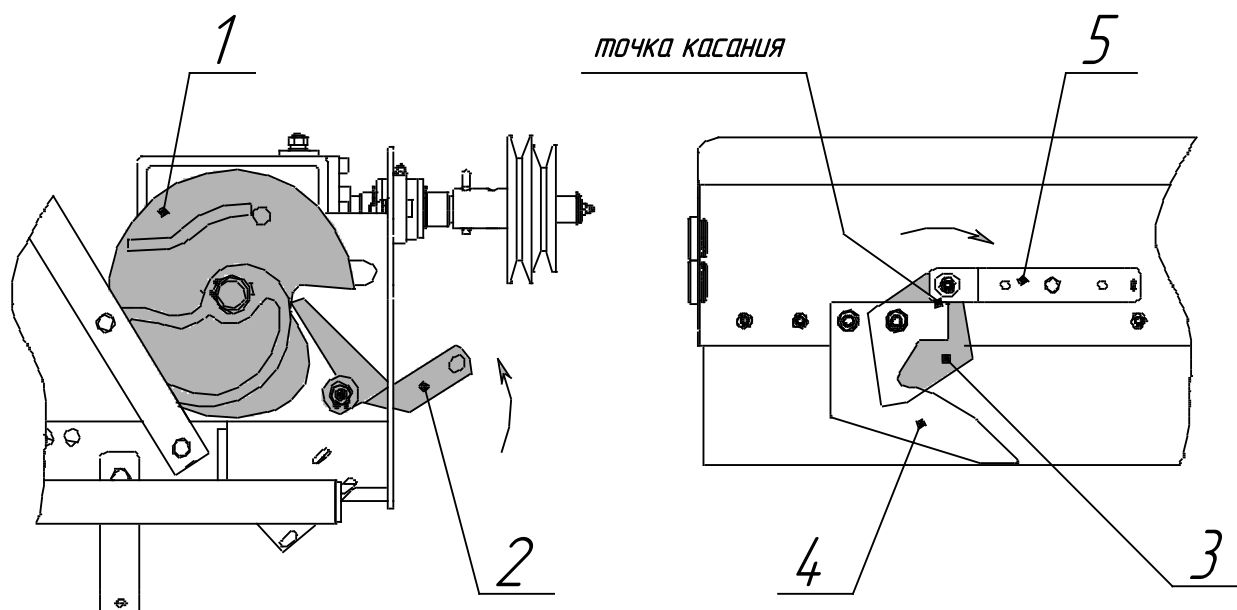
Настройка режущего механизма: 1 – эксцентрик; 2 – рычаг привода режущего устройства; 3 – нож режущего механизма; 4 – противорежущая пластина; 5 – рычаги привода ножей.
